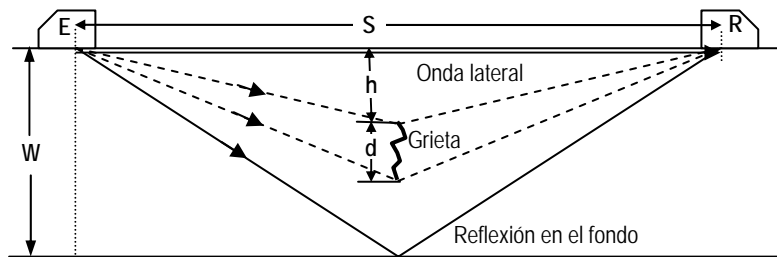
Geometría para el cálculo de la dimensión y posición de una grieta.
